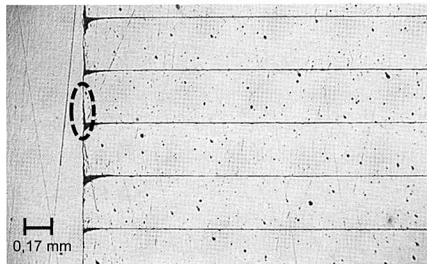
Schnittansicht eines in ein Gehäuse eingepressten Blechpakets
